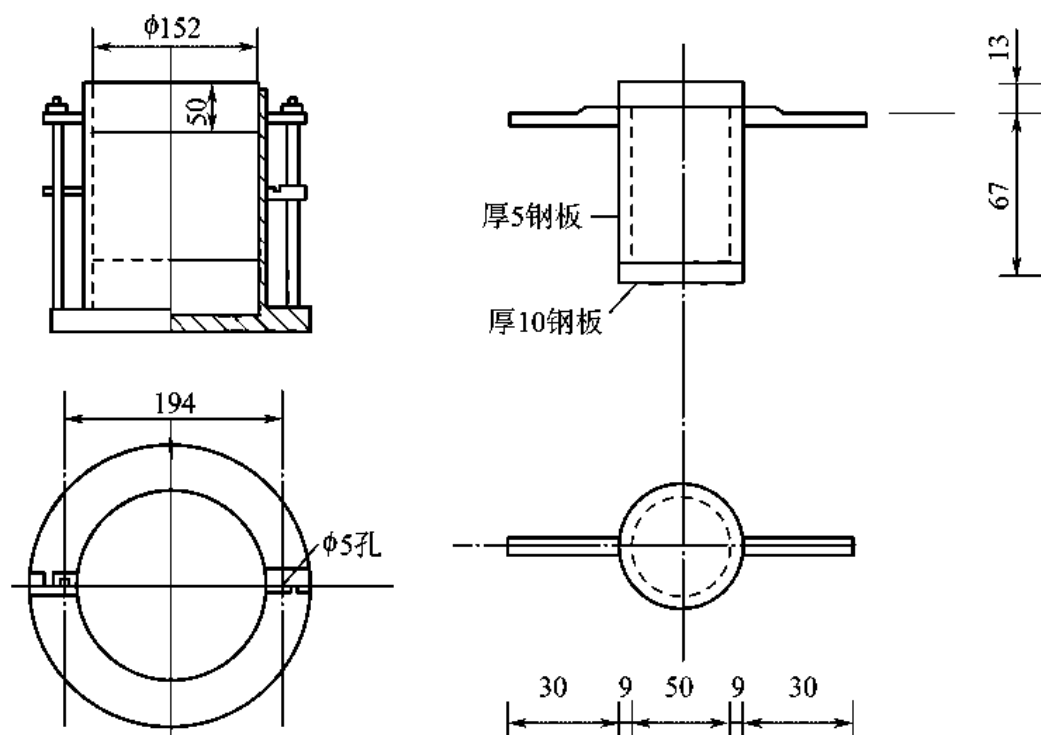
试样筒(单位:mm) 图 15.2.1-3 承载板(单位:mm)
